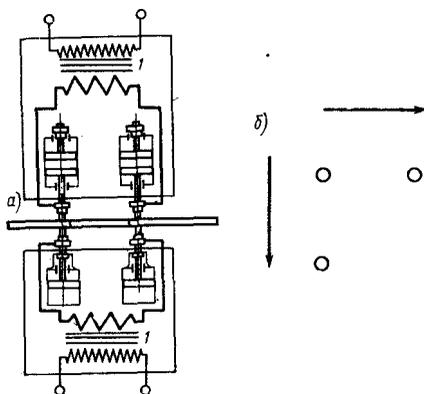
Точечная контактная сварка плоских узлов:
